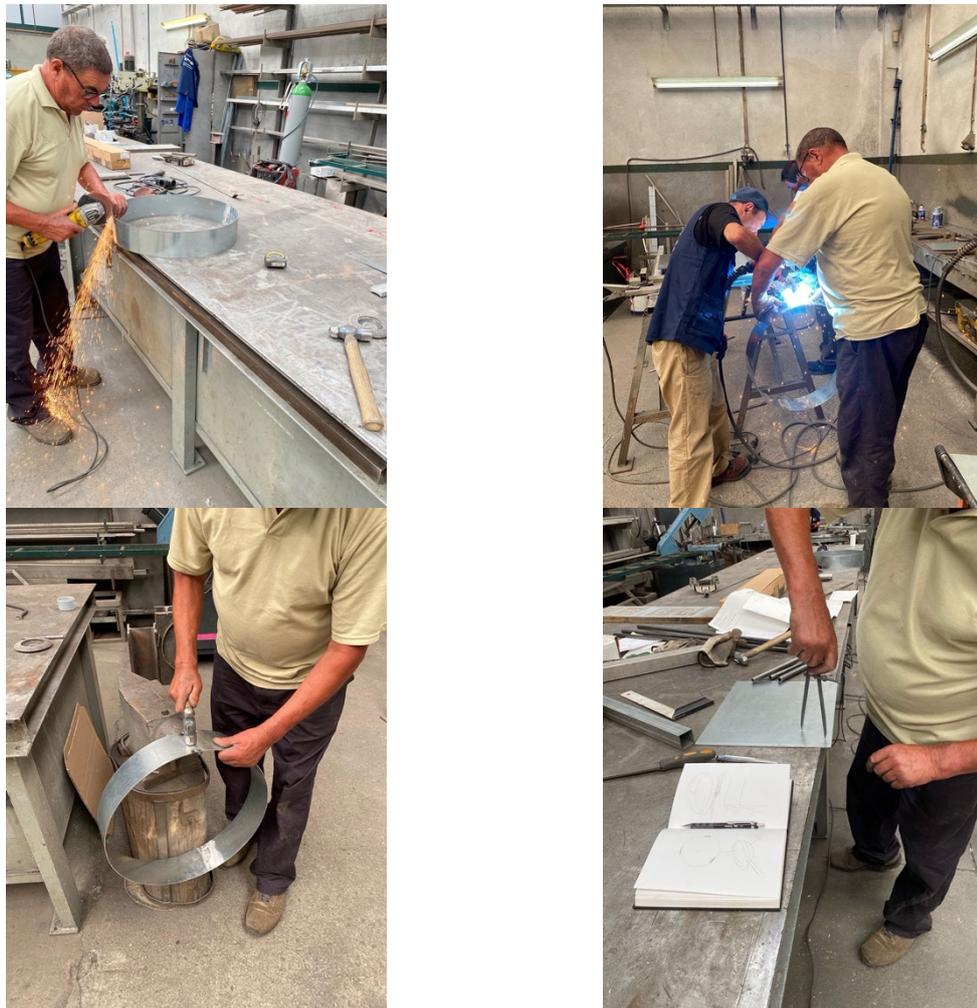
Soldadura do aro e elaboração inicial da chapa da base
